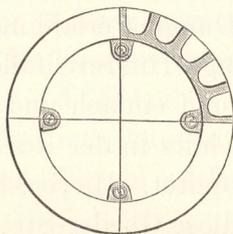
Horizontale Säscheibe der Kartoffellegemaschine von Gebr. Adam, Greifenhagen.
